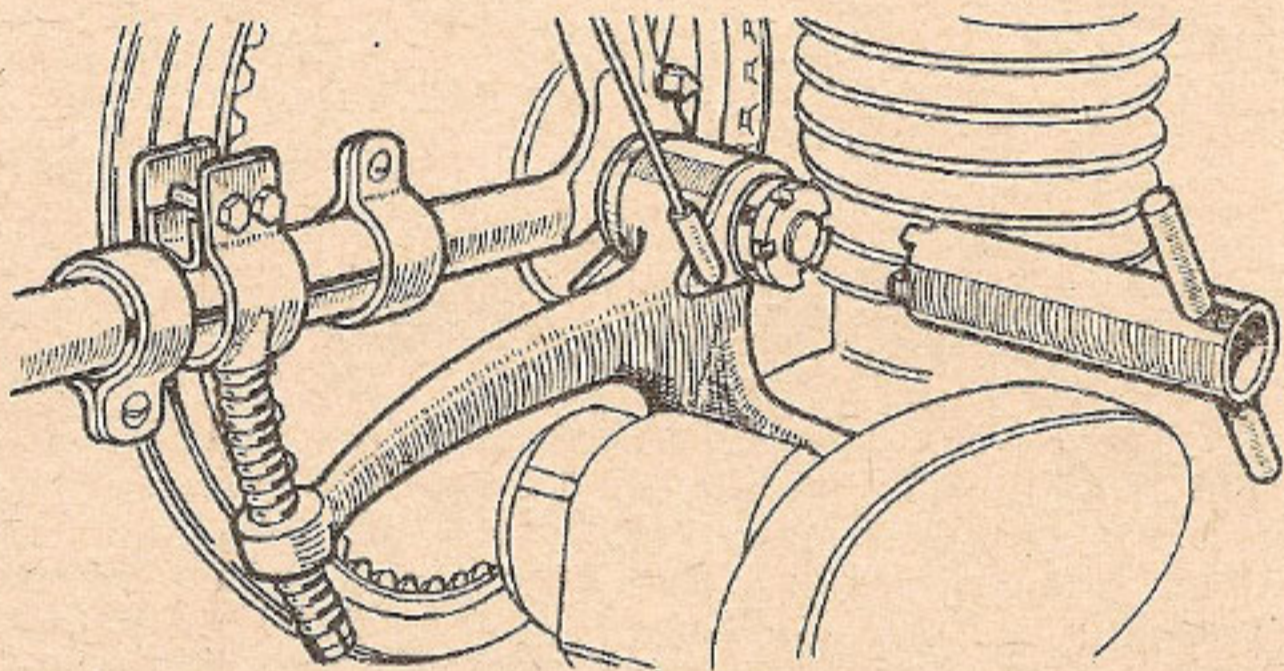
DÉMONTAGE DU MOTEUR (VAP 3)
